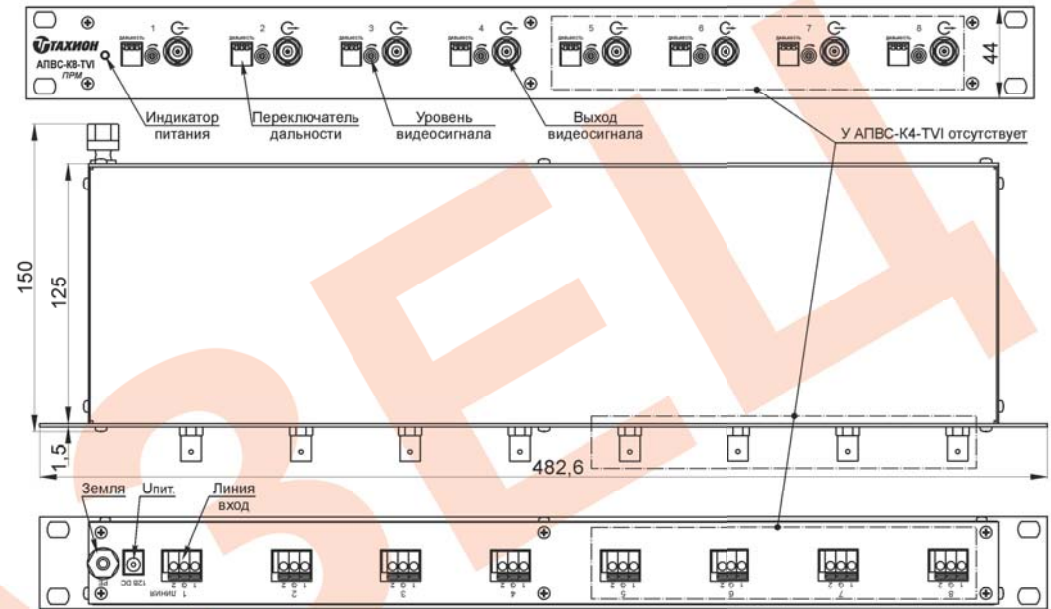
Устройство и габаритные размеры АПВС-К8-TVI
